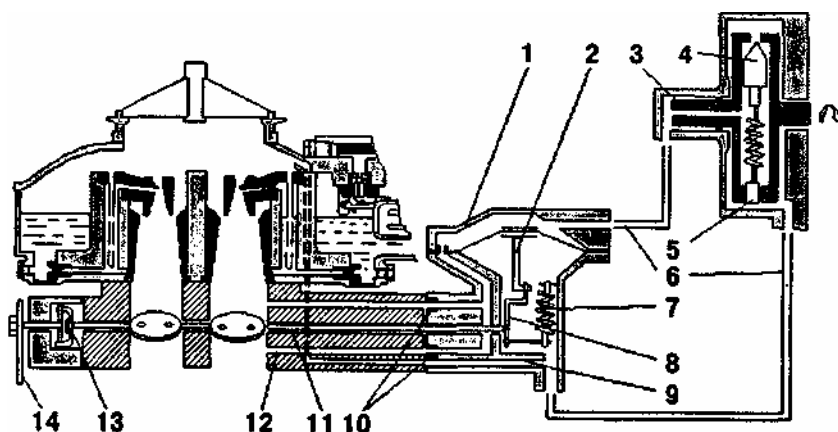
Схема пневмоцентробежного ограничителя частоты: 1 - исполнительный механизм ограничителя; 2 - мембрана со штоком; 3 - ротор центробежного датчика; 4 - клапан; 5 - винт настройки датчика; 6 - соединительные трубки; 7 - пружина ограничителя; 8 - двуплечий рычаг; 9 - канал в
